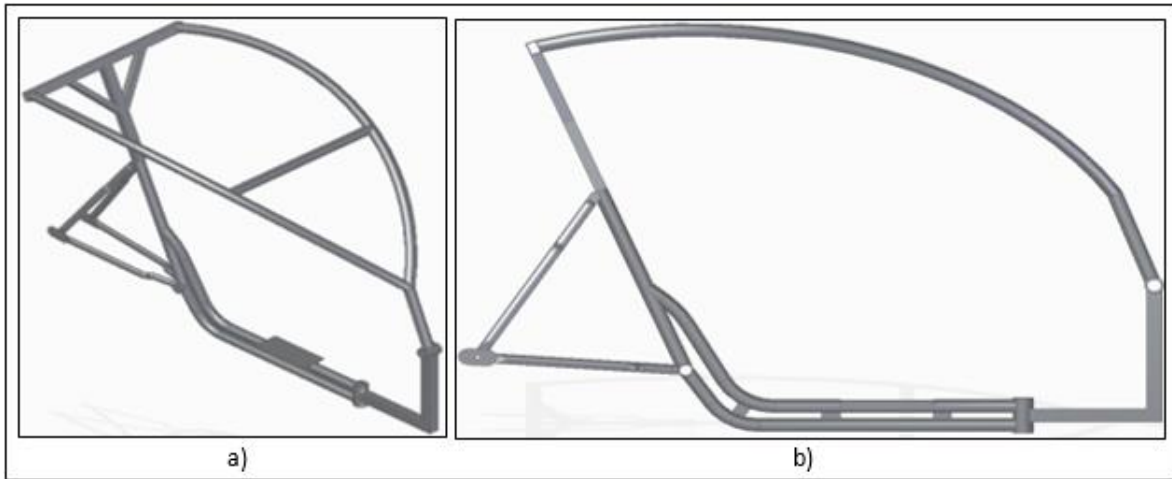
Diseño CAD 3: a) vista isométrica y en vista lateral.
